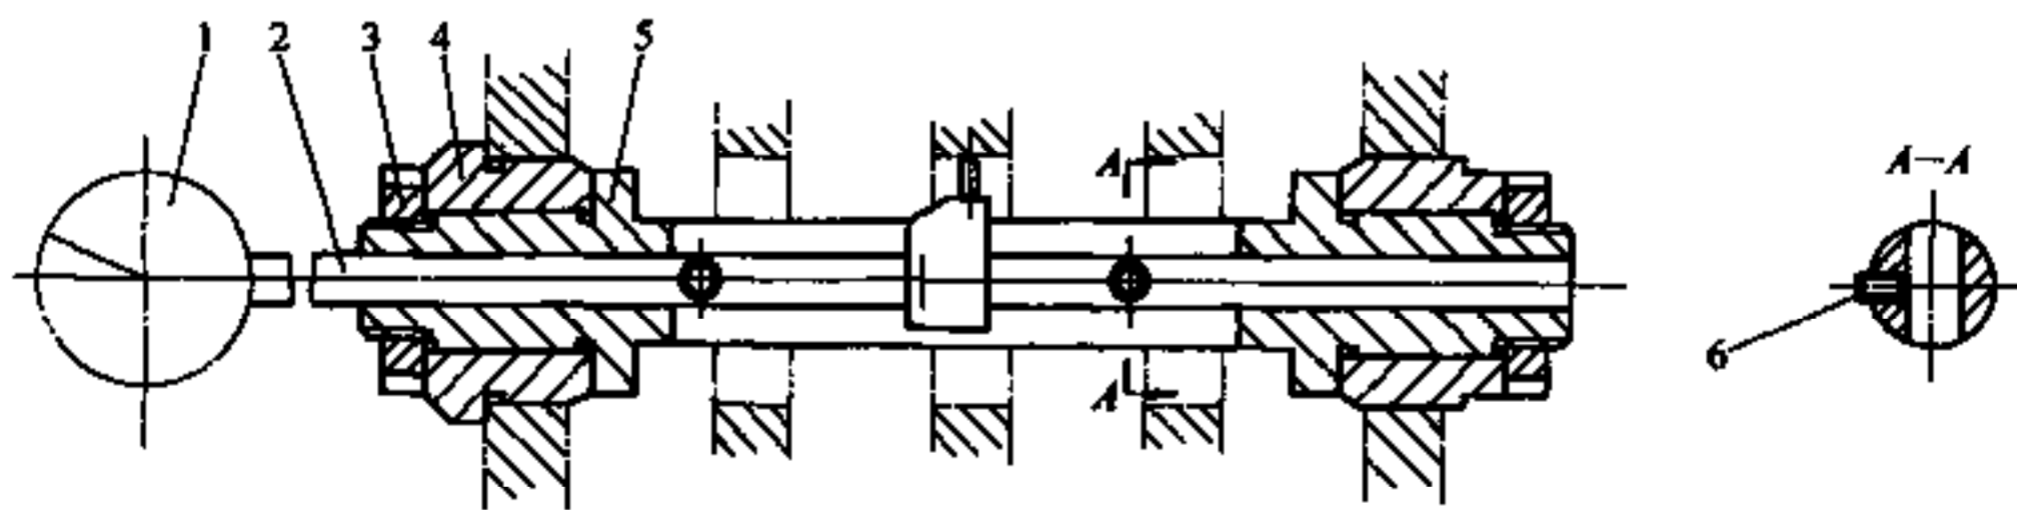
机体各中间轴承孔对两端轴承孔同轴度检具
